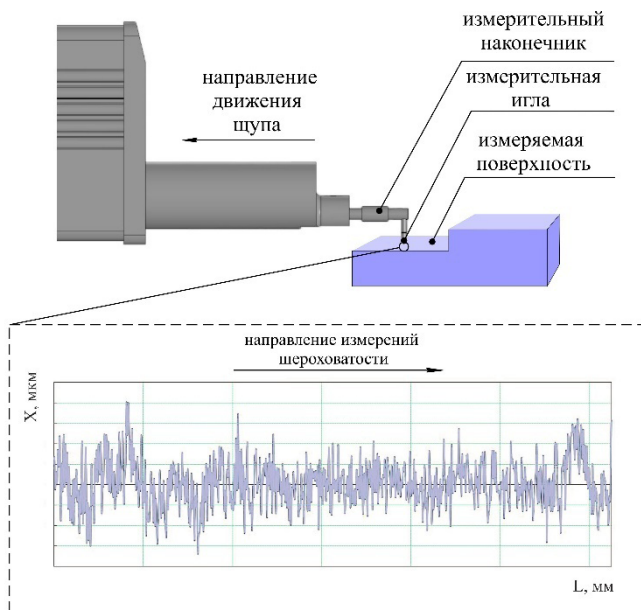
Схема процесса измерений шероховатости поверхности образца после выполнения фрезерования
